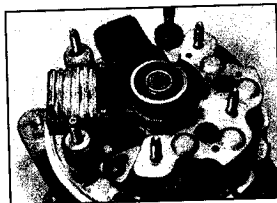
Нагрев подшипника для облегчения снятия задней крышки (См. Раздел 8)
